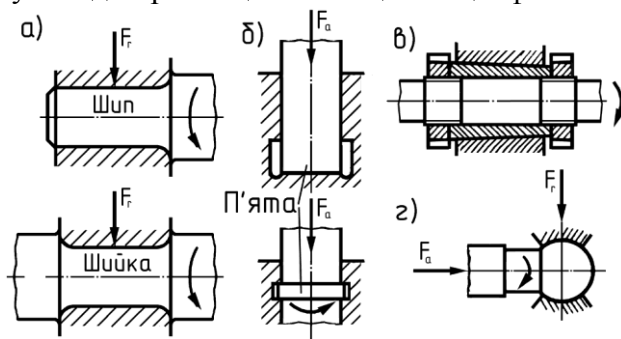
Форма робочої поверхні підшипників ковзання: *а* – циліндрична; *б* – плоска; *в* – конічна; *г* - сферична
